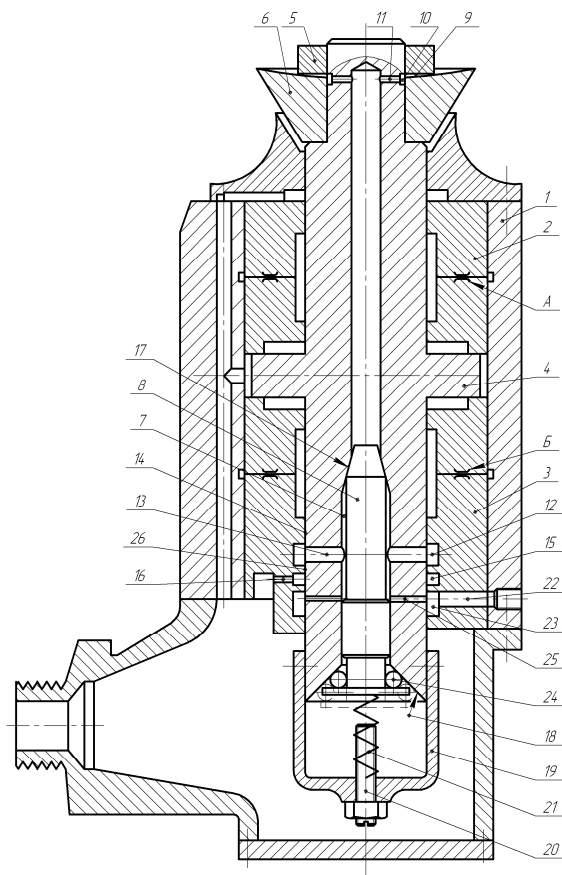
Ротационный резец для высокоскоростной токарной обработки нежестких валов
